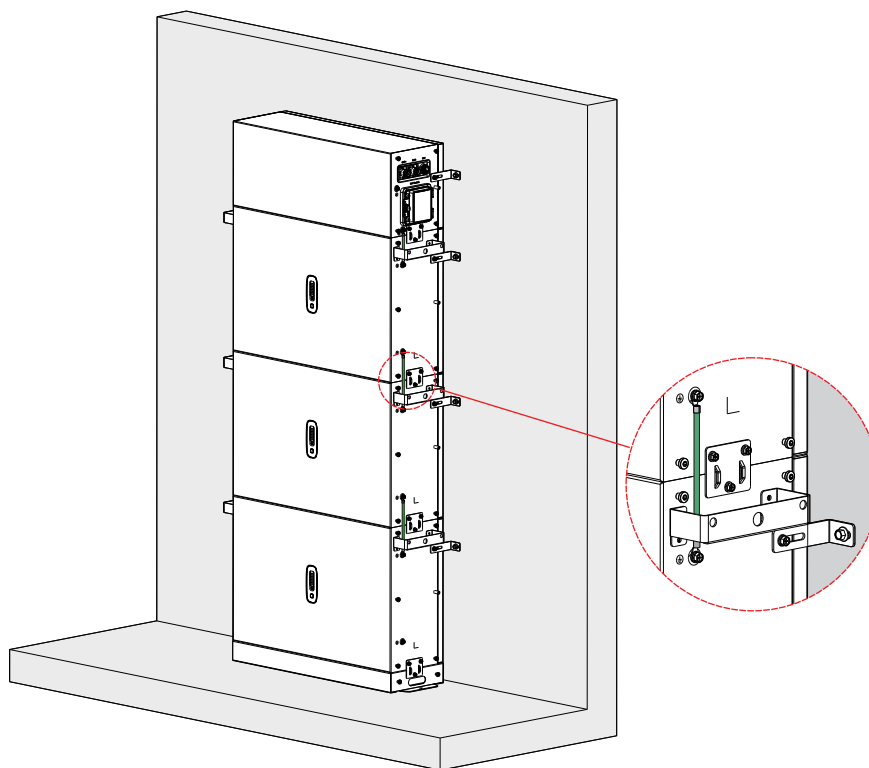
Collegamento del cavo di protezione di messa a terra interno
